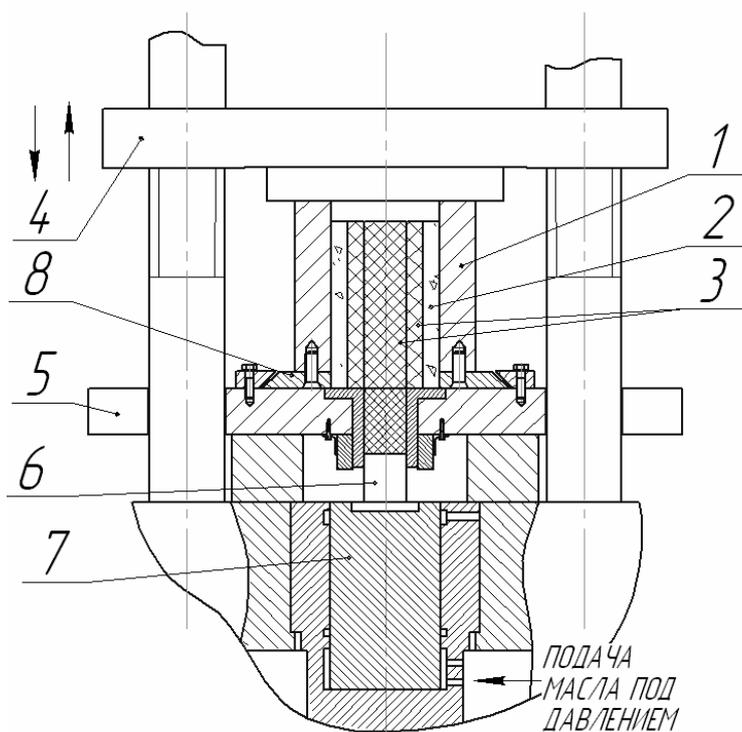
Принципиальная схема установки для ЭСП трубчатых изделий из порошков: 1-контейнер, 2-порошок, 3-эластичный формующий элемент, 4- подвижная траверса, 5-опорная плита, 6- пуансон, 7-плунжер, 8-подвижная плита
